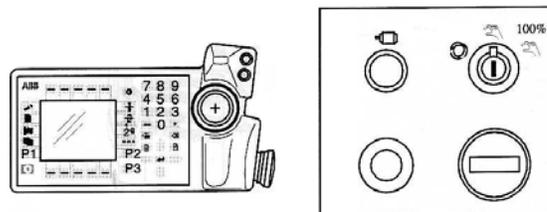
Teach Pendant (izquierda) y panel del operador (derecha).
